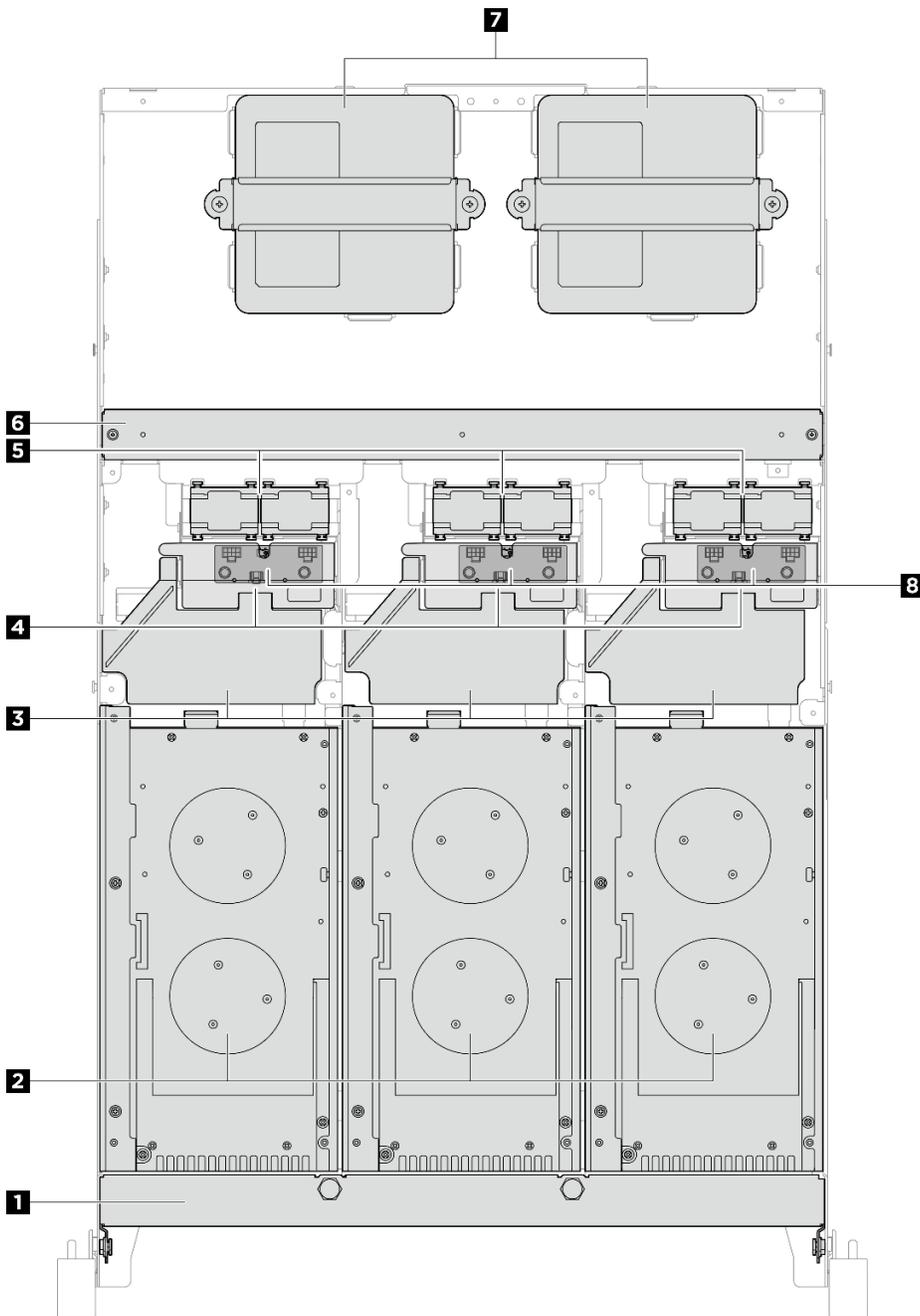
Вид сверху корпуса ThinkEdge SE100 1U3N
